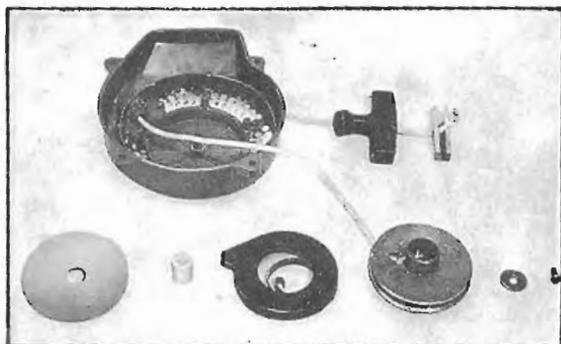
Despiece del dispositivo de arranque (JONSE-REDS).
